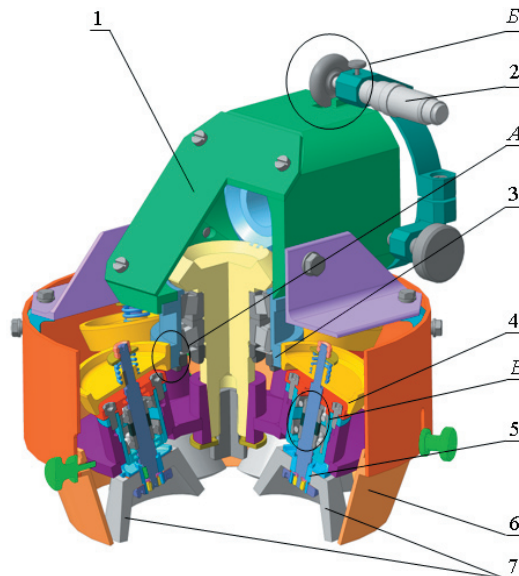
Конструкция торцевой планетарно-шлифовальной головки
